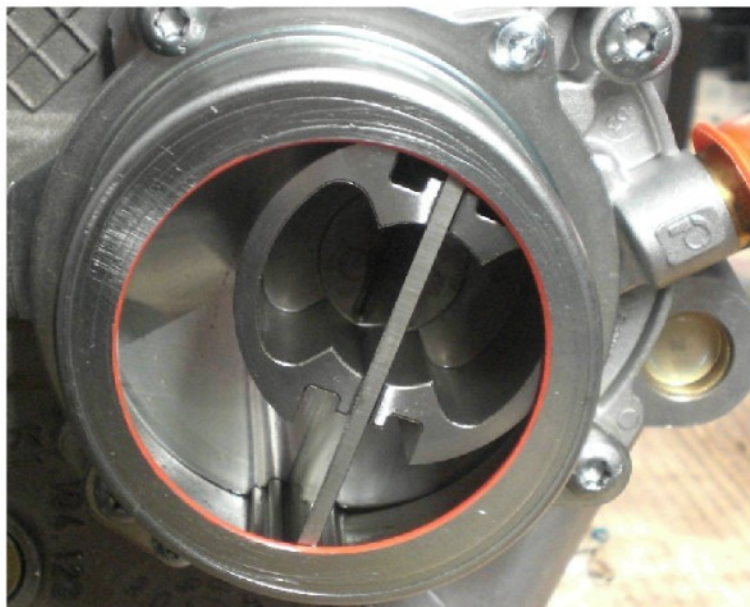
Řez hlavním olejovým čerpadlem | foto dokumentace autora |
